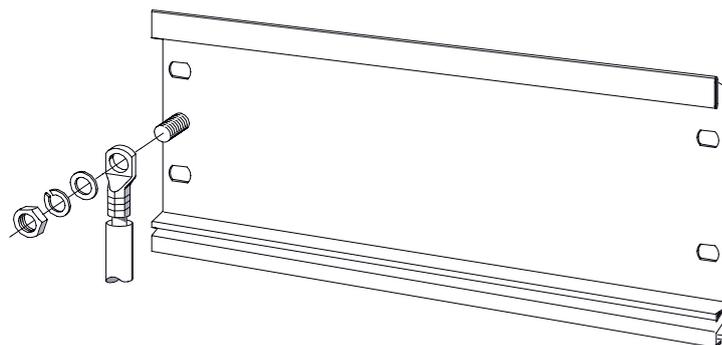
Collegamento del conduttore di protezione sulla guida profilata
